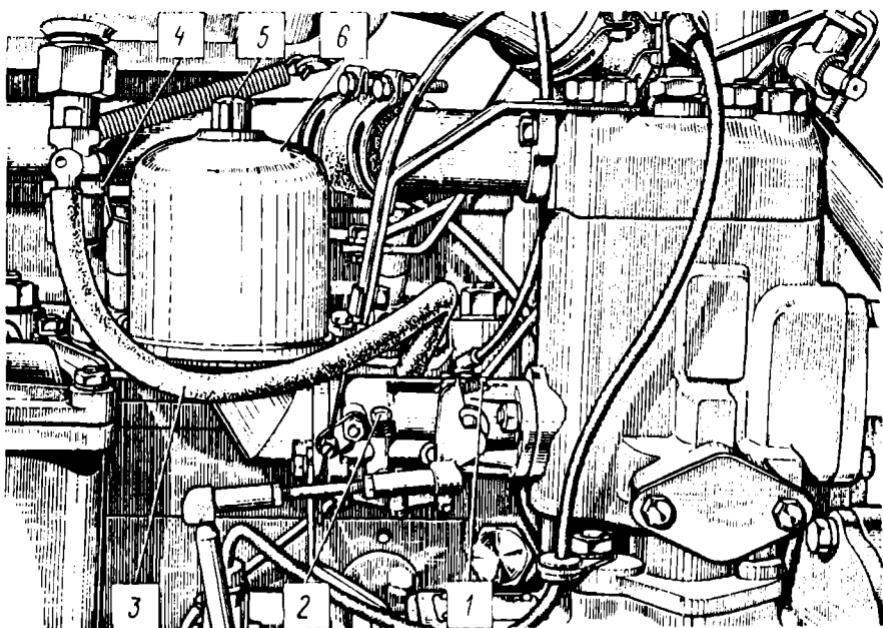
Воздухоочиститель и карбюратор пускового двигателя;
